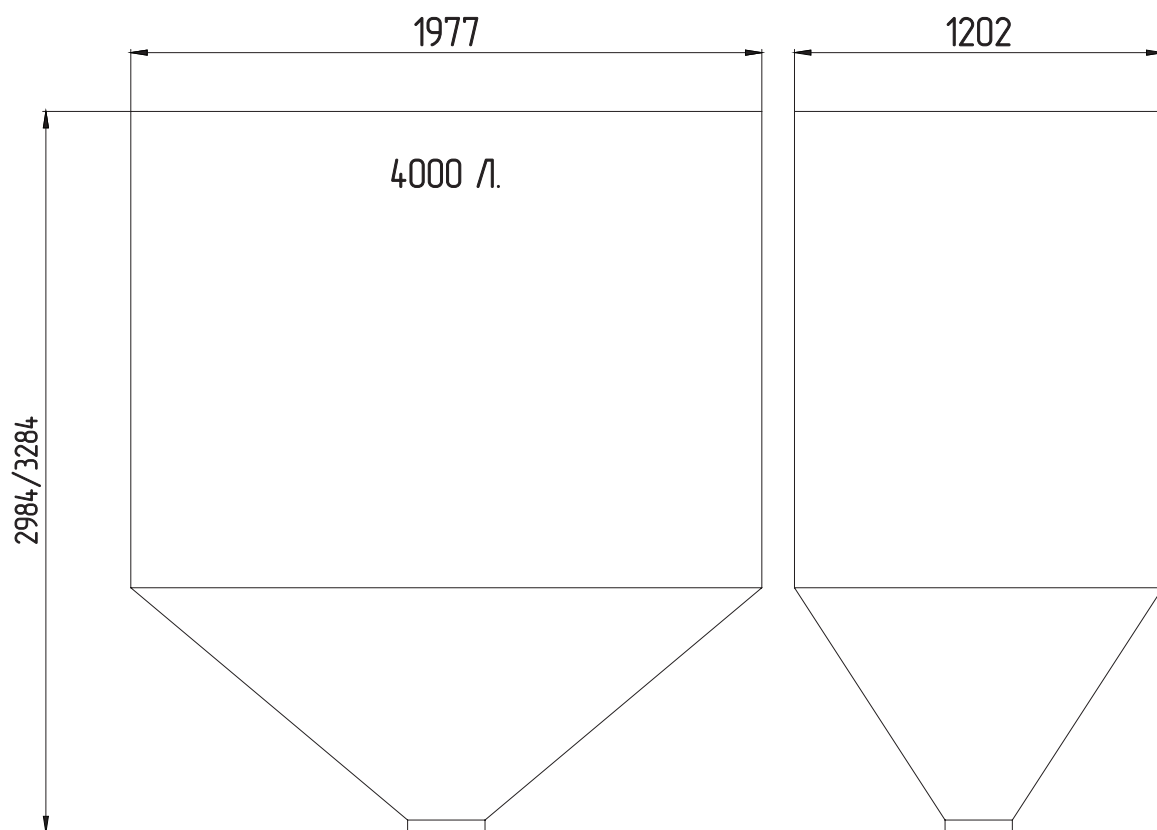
Габаритные размеры топливного бункера 4000 л 1 горло
